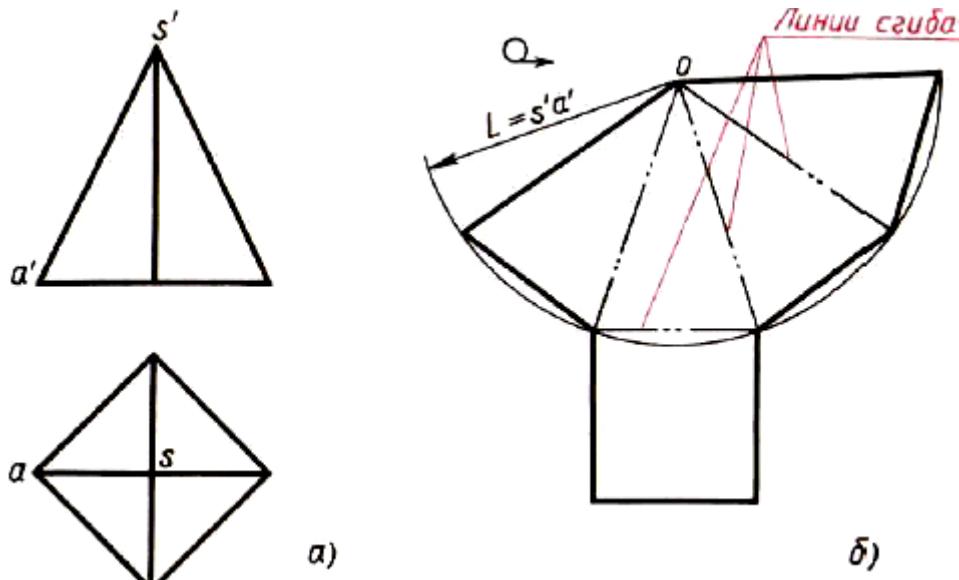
Построение чертежа развертки поверхностей пирамиды: а — два вида; б — развертка поверхностей
